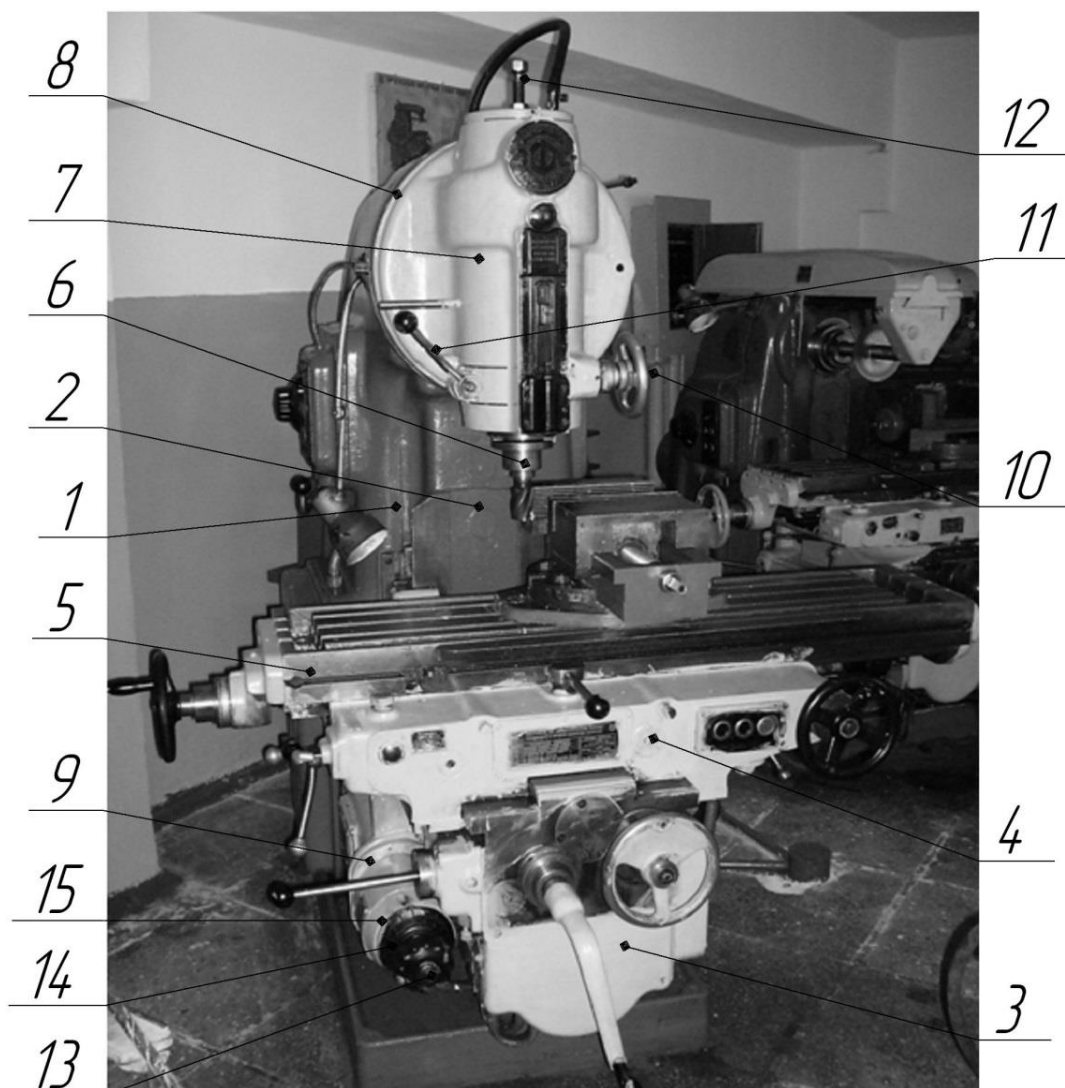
Общий вид станка 6М12П: 1 – станина; 2 – направляющие станины; 3 – консоль; 4 – салазки поперечные; 5 – стол; 6 – шпиндель; 7 – шпиндельная головка; 8 – лимб; 9 – механизм переключения подач; 10 – маховик ручного перемещения шпинделя; 11 – рукоятка, фиксирующая положение гильзы; 12 – винт; 13 – кнопка; 14 – диск; 15 – лимб
